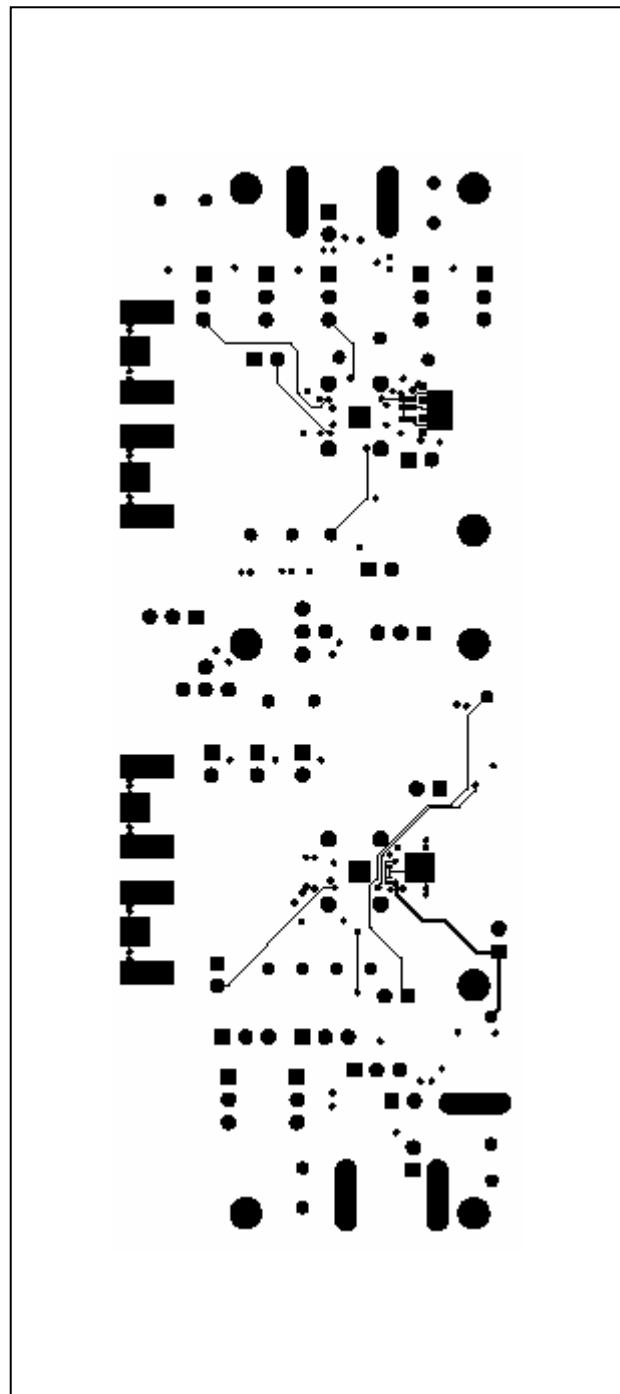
MAX3738 评估板 PCB 布局—焊接层
